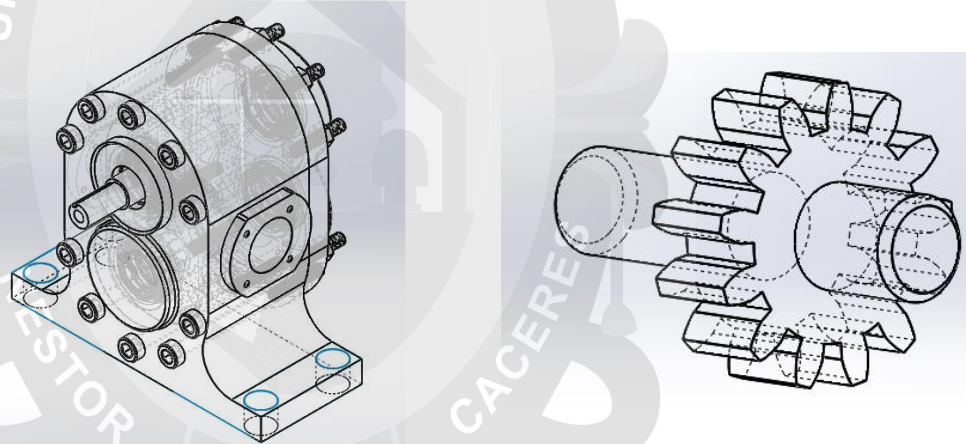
Diseño de la bomba hidráulica y su engranaje
